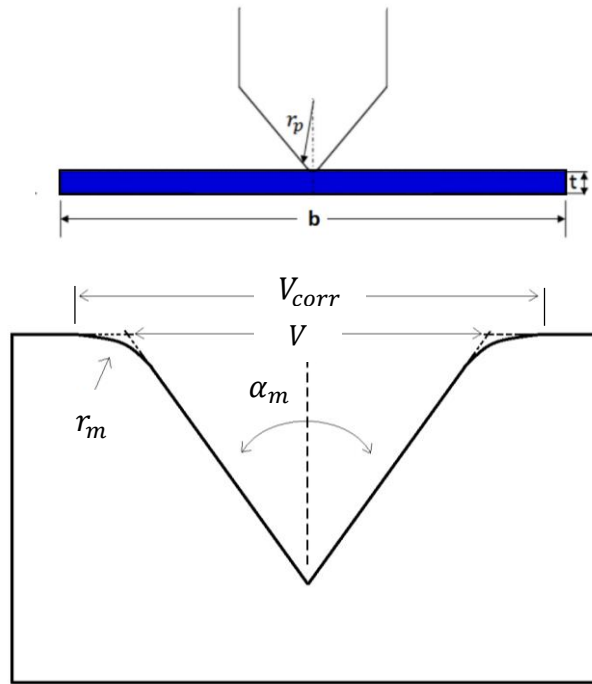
Variáveis geométricas das ferramentas de quingem.
